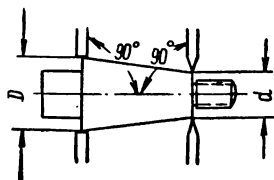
Схема проверки размеров конической поверхности губками штангенциркуля.
